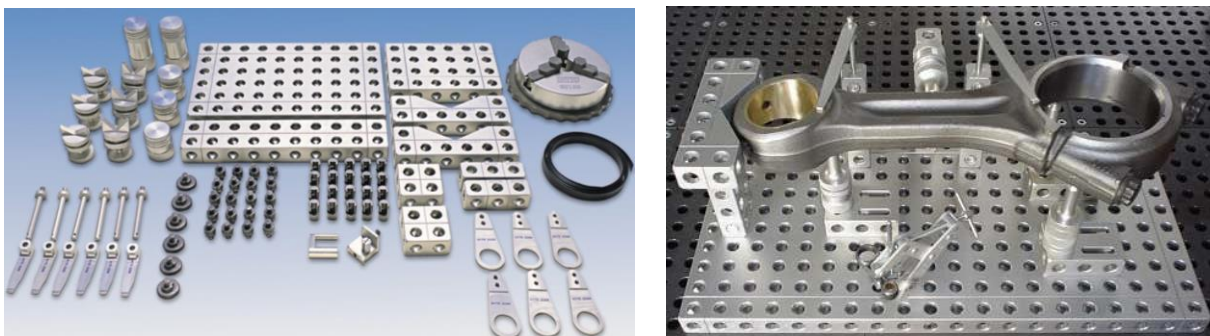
53 – Mitutoyo – Eco – fix – car – fix [19]
